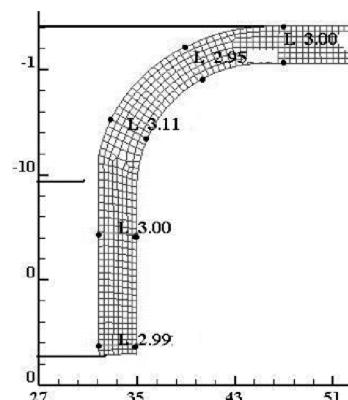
Кінцеві розміри (L) в міліметрах відбортованої частини заготовки
